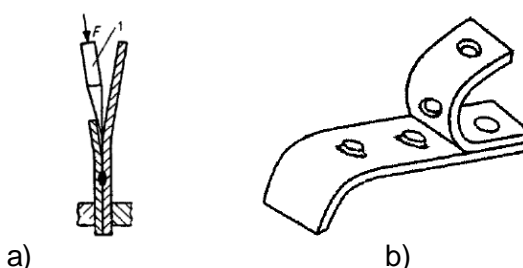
(a) Separação das chapas soldadas; (b) Lentilhas ou pepitas de solda
